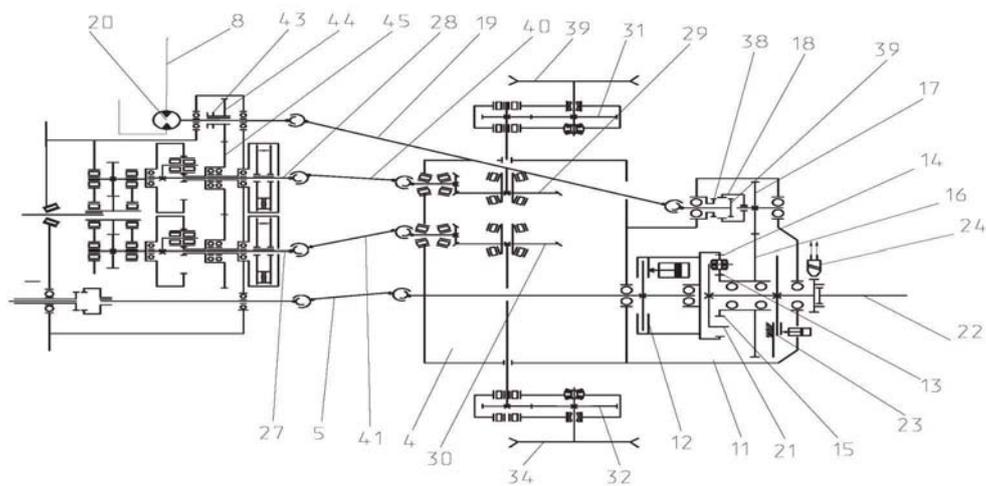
Кинематическая схема редуктора привода заднего ВОМ гусеничного трактора (обозначения на рис.8)
